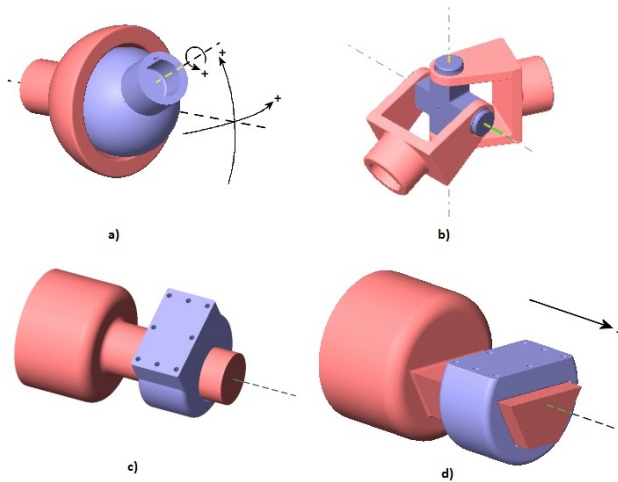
Exemplos de juntas mecânicas indicando os seus movimentos principais: a) junta esférica; b) junta universal; c) junta cilíndrica; e d) junta prismática.
